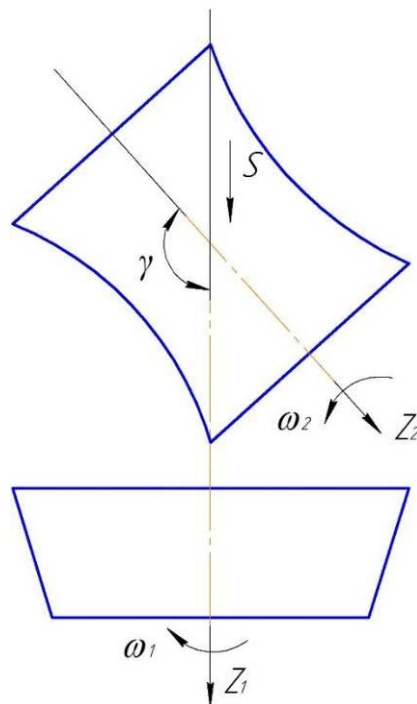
Четвертий тип схеми формоутворення 3-го класу
